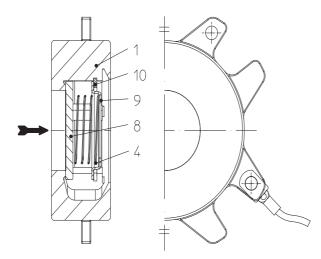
CHECKO[®]-D PN40 - Дисковый обратный клапан 1.4408
